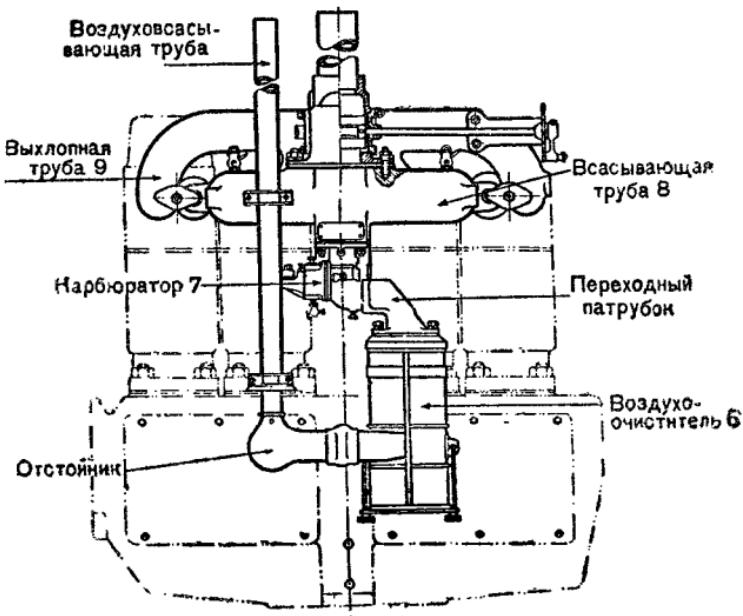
Схема расположения воздухоочистителя с воздуховасывающей трубой, карбюратора, всасывающей и выхлопной труб.
